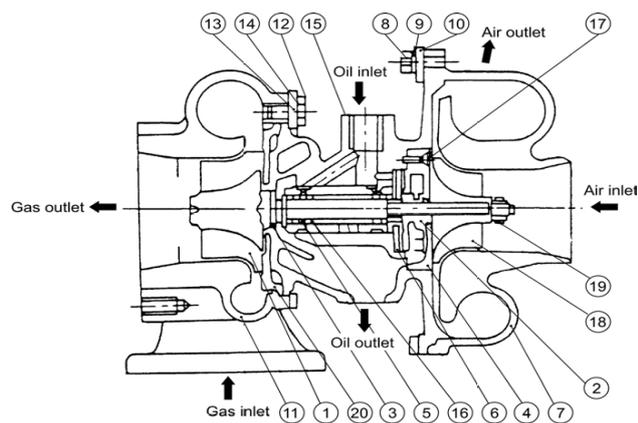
CHRA (Center Housing & Rotation Assembly)
